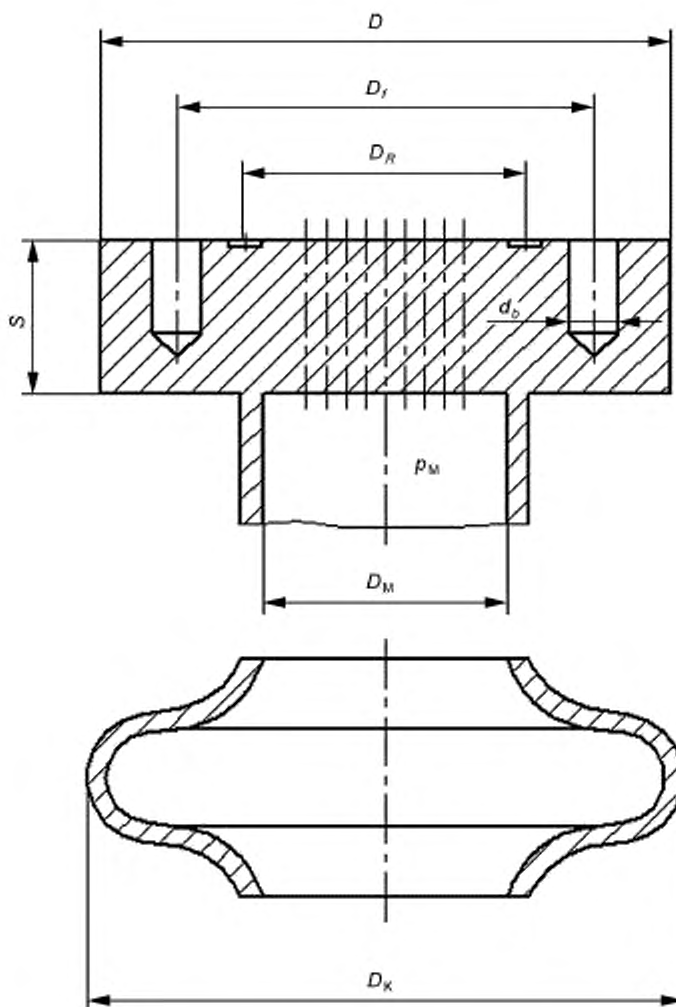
Схема оборудования с компенсатором на корпусе и трубной решеткой с разъемным соединением с корпусом
